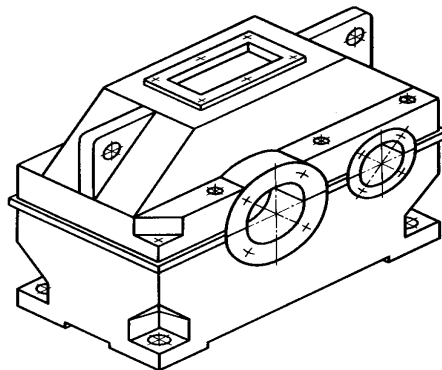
Корпус одноступенчатого цилиндрического редуктора
